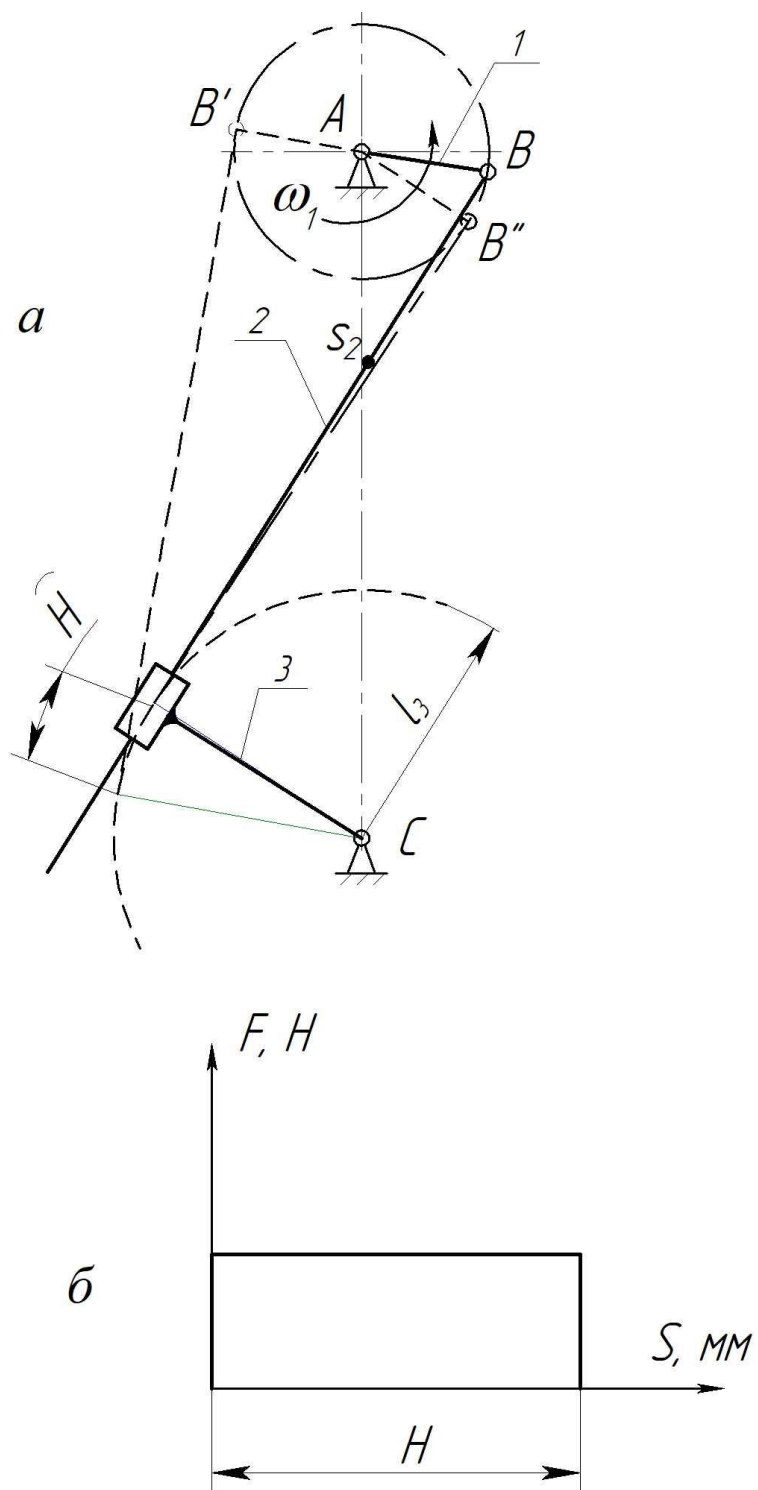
Схема механизма зубострогального станка для обработки прямозубых конических колес
